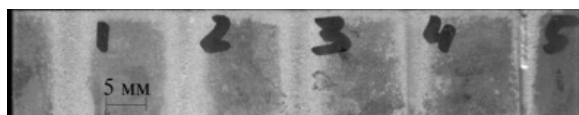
Зразок обробленої пластини з канавками при використанні дроту діаметром 0,15 мм; МЕР, мм: 1 – 0,5; 2 – 0,3; 3 – 0,2; 4 – 0,1; 5 – 0,05
